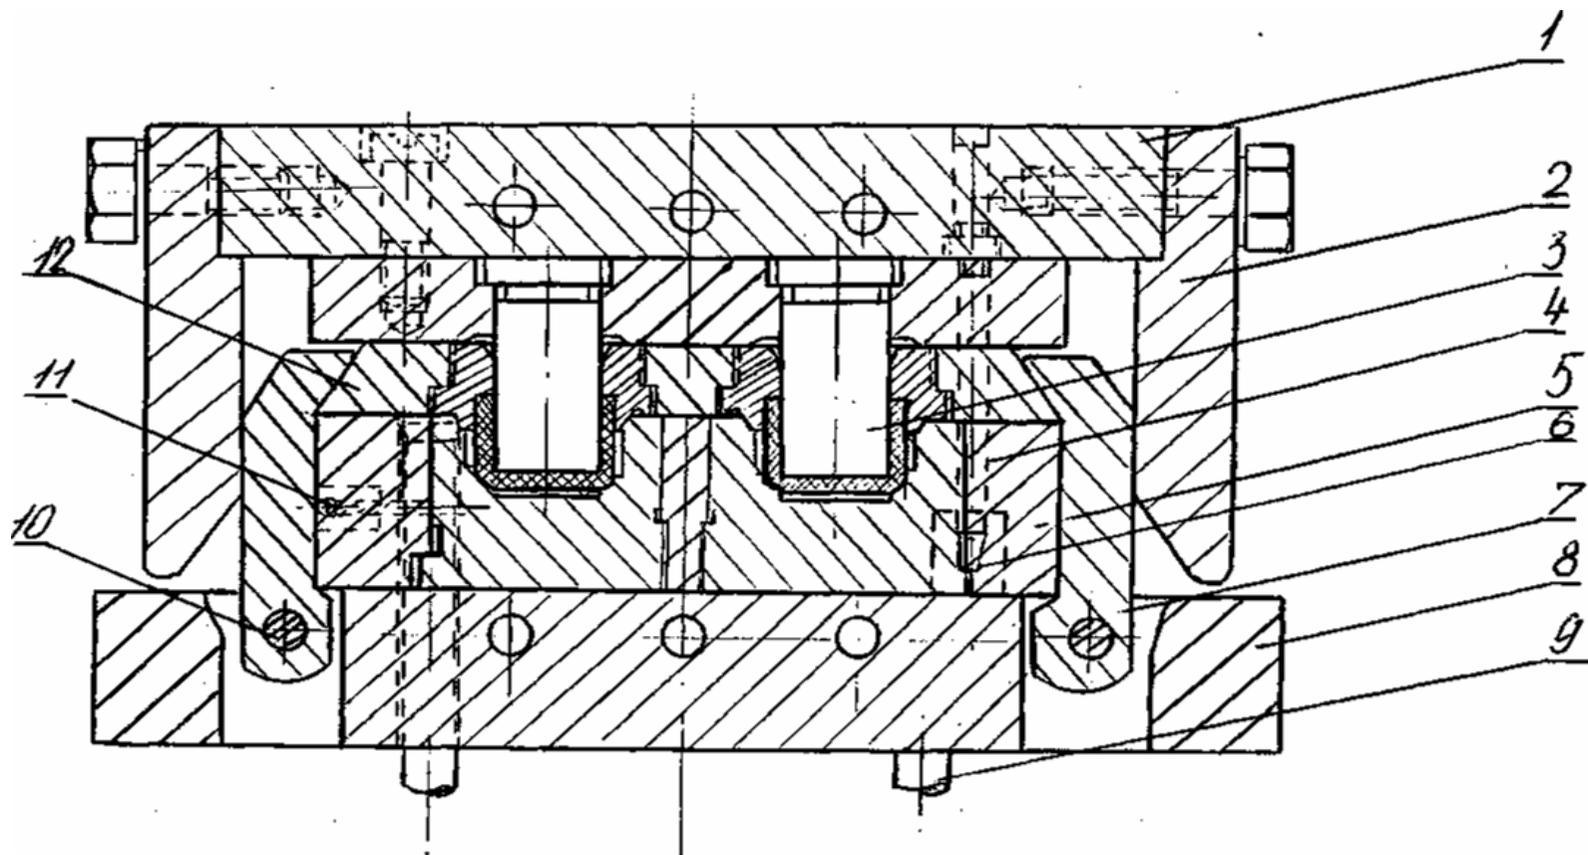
Пресс-форма для изготовления деталей методом прессования:
